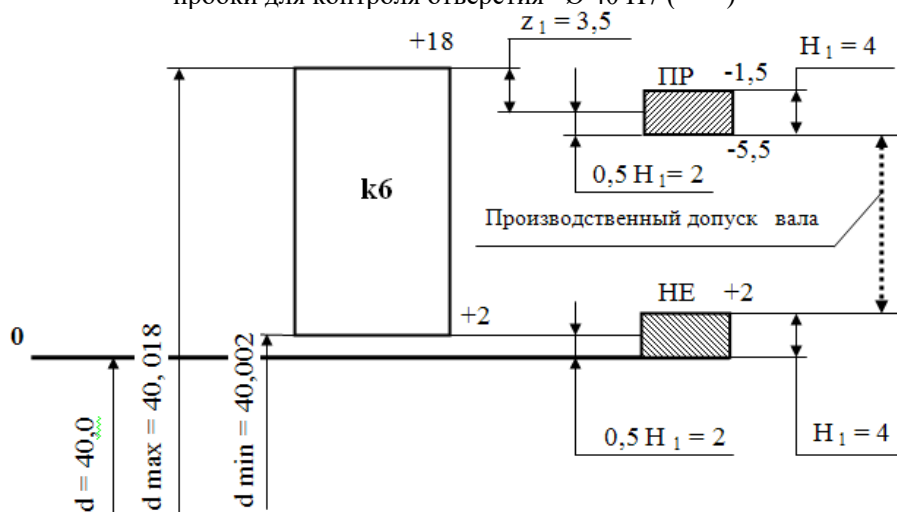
Схема расположения полей допусков на изготовление калибра - скобы для контроля вала $\varnothing 40 k6 (+0,018)$
